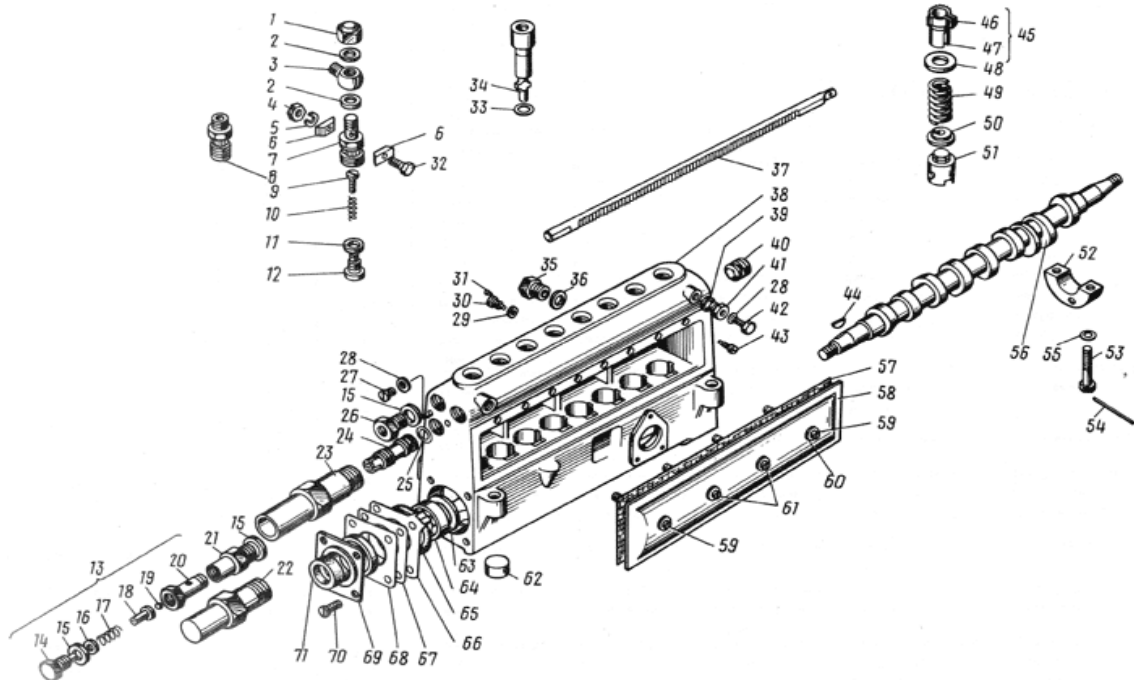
Паливний насос високого тиску двигуна ЯМЗ-238: 1-гайка ковпачкова; 2, 5, 15, 16, 25, 28, 29, 36, 39, 60, 63 - шайби; 3 - ніпель; 4 - гайка; 6-сухарь; 7,8-штуцер; 9-упор клапана; 10, 17, 49 - пружина; 11, 57, 67, 68 - прокладка; 12 і 13 - клапан нагнітальний і перепускний; 14 - пробка; 18 - напрямна клапана; 19 - шарик $d=6,35$ мм; 20 - корпус клапана; 21, 26, 35 - ввертиш; 22 - ковпачок рейки; 23 - ковпачок клапана; 24 - штуцер; 27, 30, 43, 59, 61, 70 - гвинт; 31 - стопор; 32, 53 - болт; 33, 55, 65 - кільце-ущільнювач; 34 - пара плунжерна; 37 - рейка; 38 - корпус паливного насоса; 40 - пробка; 41, 42 - пробка випуску повітря; 44 - шпонка; 45, 46 - вінець зубчатий; 47 - втулка вінця; 48, 50 - тарілка верхня і нижня; 51 - штовхач плунжера; 52 - опора кулачкового валу; 54 - шплінт; 56 - вал кулачковий; 58 - кришка; 62 - заглушка; 64 - підшипник роликовий; 66 - показчик початку подачі палива; 69 - кришка підшипника; 71 - манжета.
